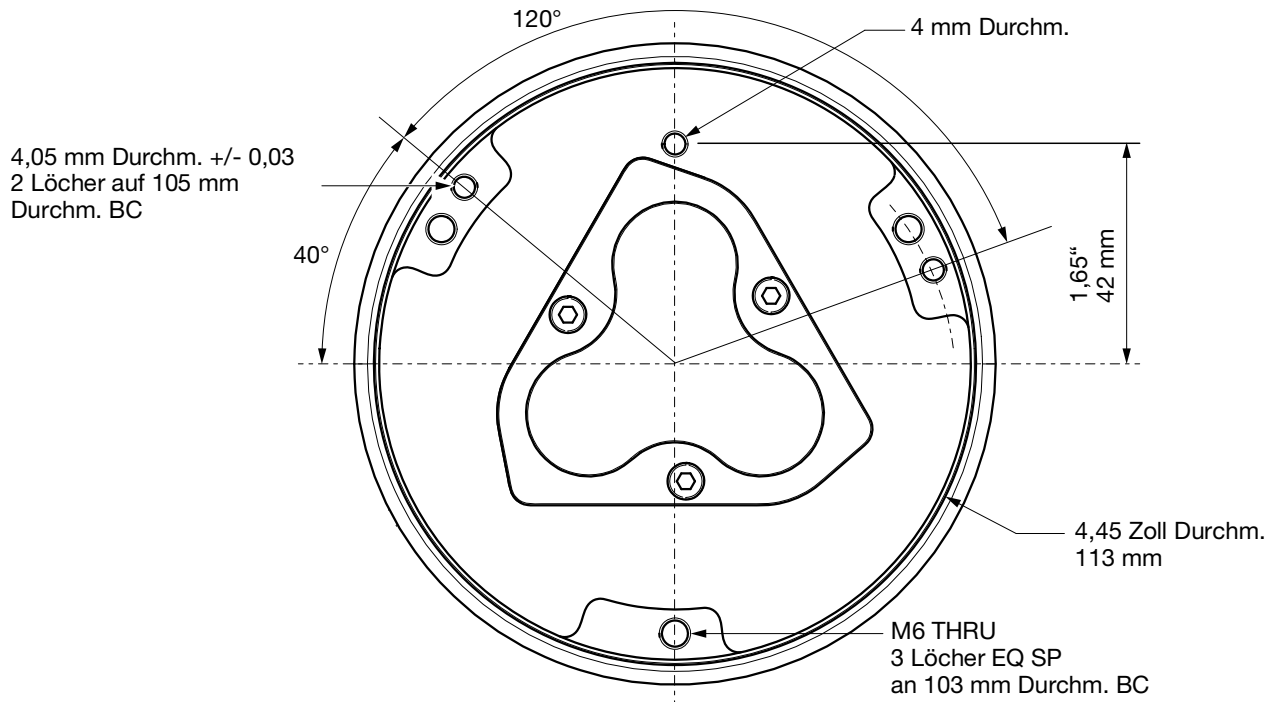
Roboter montageflansch, typisch für alle Switch 3D-Pistolen
